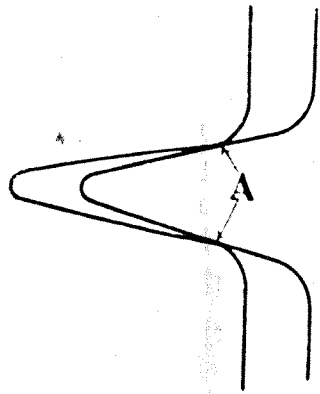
Section de rondelles Hele-Shaw, montrant l'entraînement.
